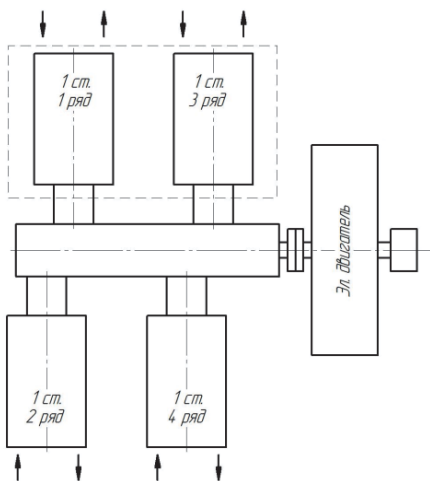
Одноступенчатый поршневой 4-х цилиндровый компрессор
